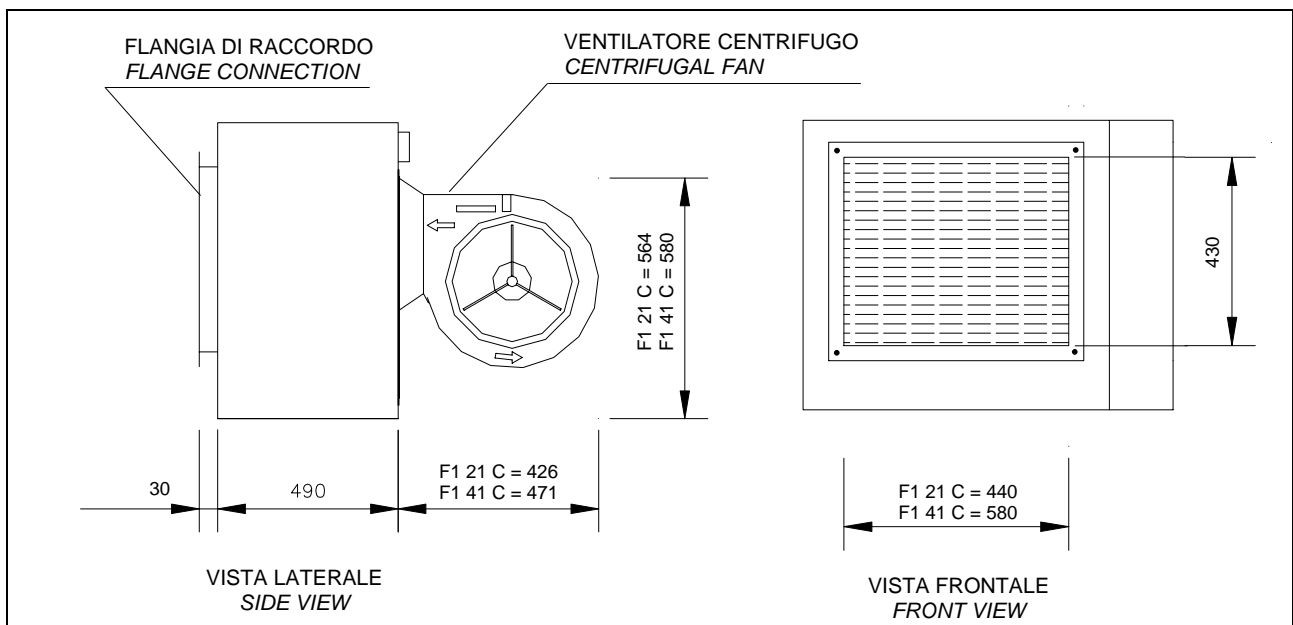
/ Figure 1 – DIMENSIONI / DIMENSIONS
